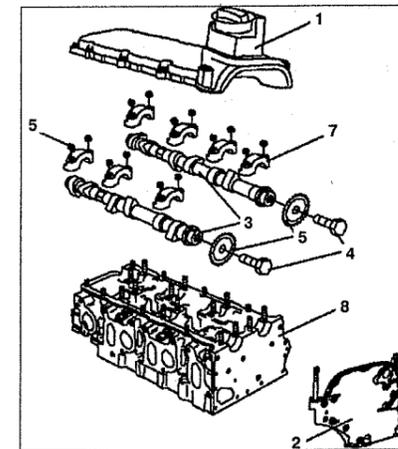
Распределительные валы: 1. Крышка головки блока цилиндров, 2. Верхняя крышка ГРМ, 3. Распределительные валы, 4. Болт, 5. Шкивы распределительных валов, 6. Гайка, 7. Крышки коренных подшипников, 8. Головка блока цилиндров.
